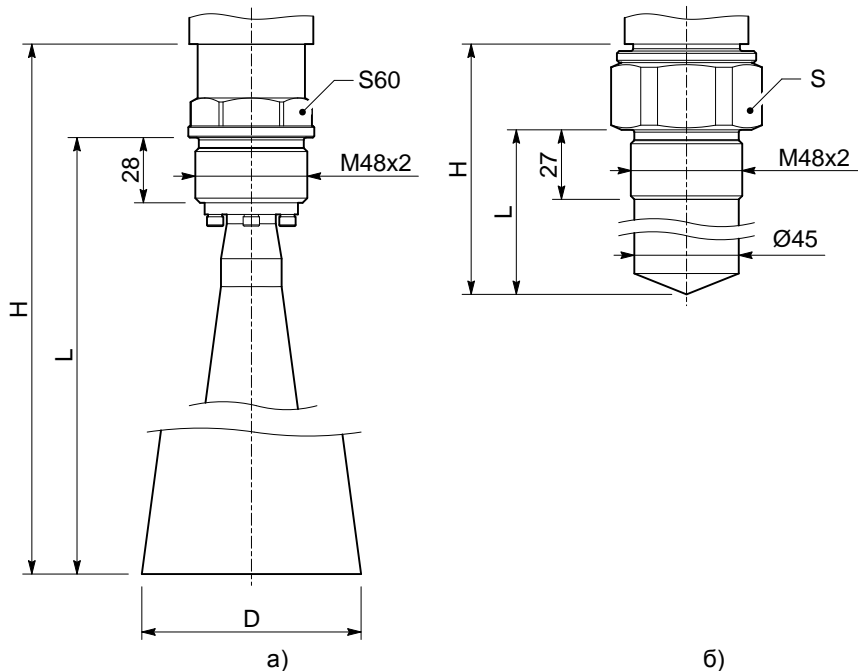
Габаритные размеры антенн с резьбовым присоединением:
